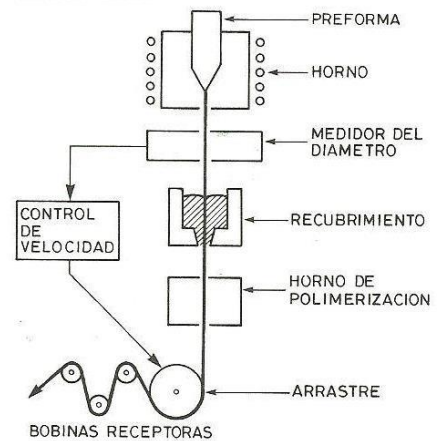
Disposición de los diversos elementos de una máquina de estirado de la preforma.
